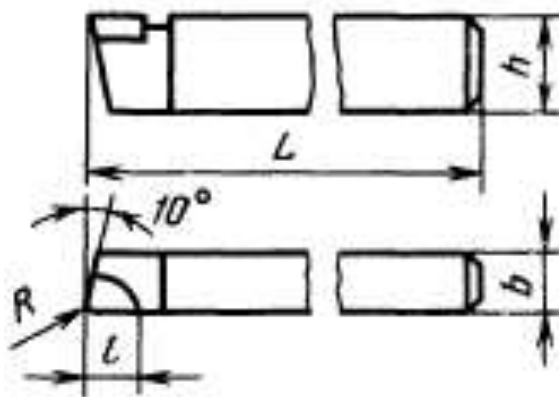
упорний різець з пластинами із твердого сплаву з кутом у плані 90° ГОСТ 18879-73
